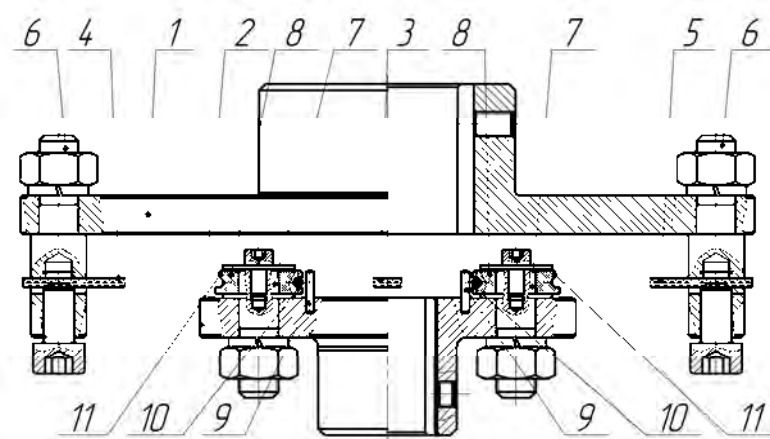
Загальний вид канатно-роликової муфти з обмежувальними штифтами
